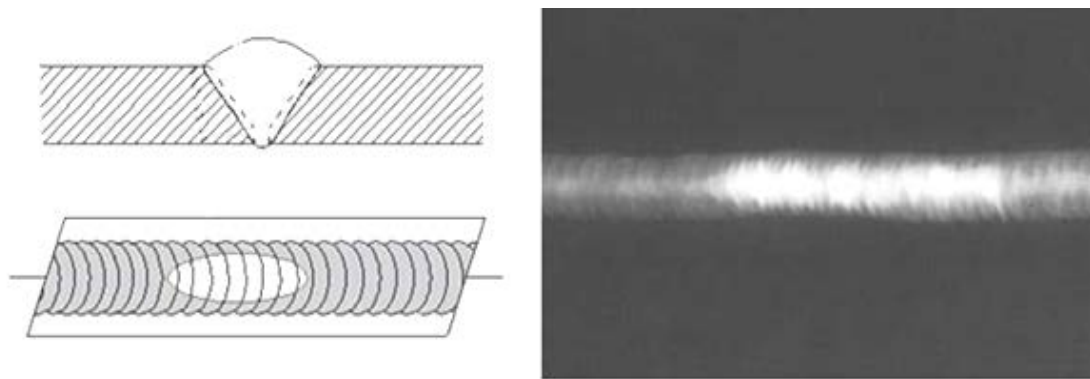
Refuerzo de Soldadura Excesivo.
